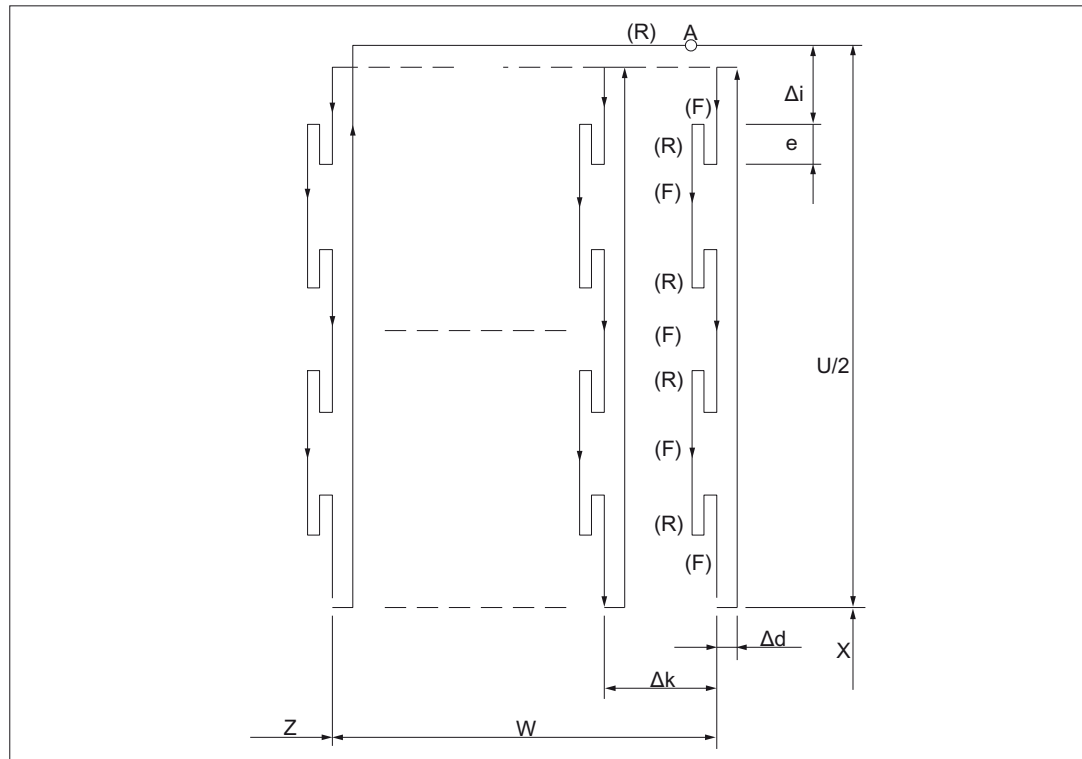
Schnittbahn beim Tieflochbohren und beim Einstechen in der Planachse (G75)
